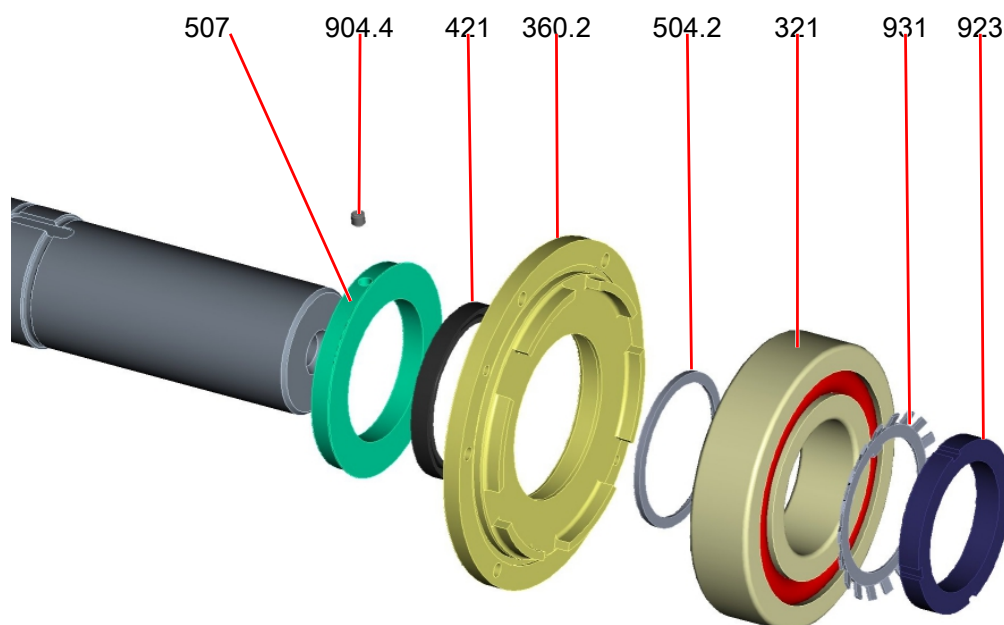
Замена подшипниковой опоры — ASP с платформой
